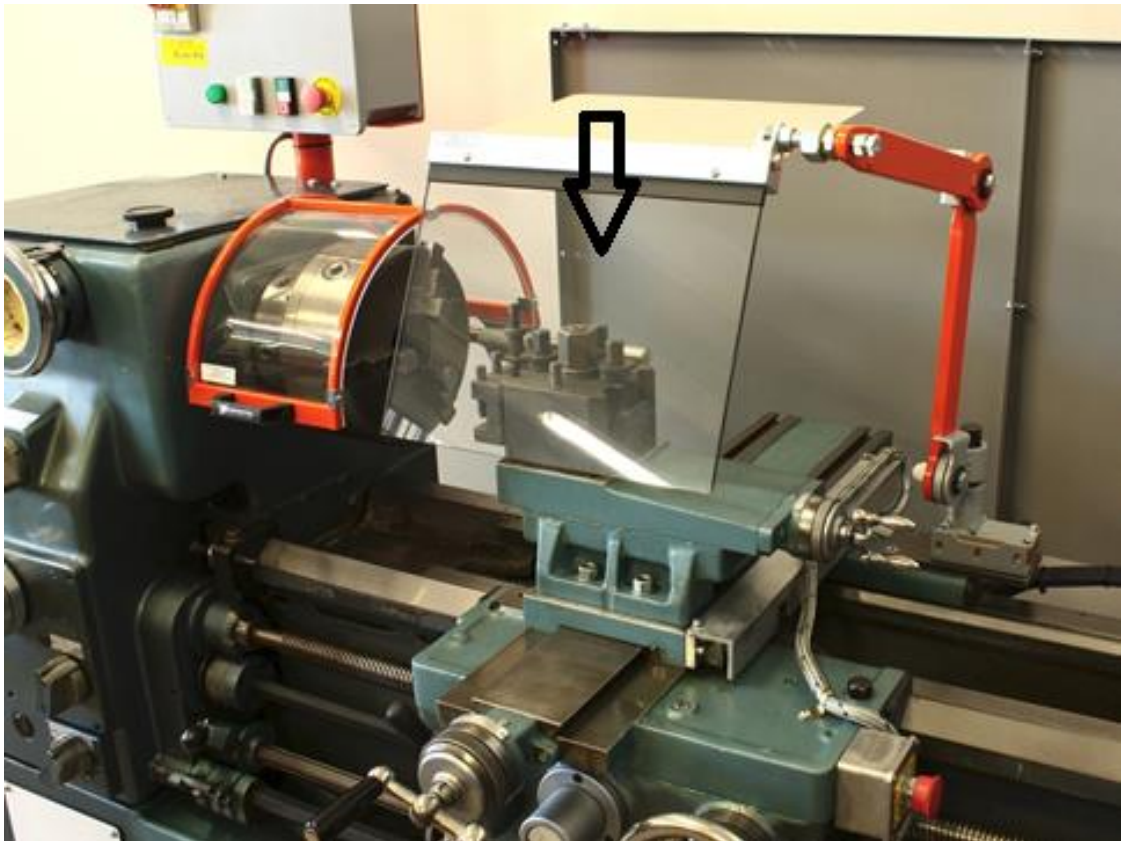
Рабочее место оператора токарного станка с ЧПУ
